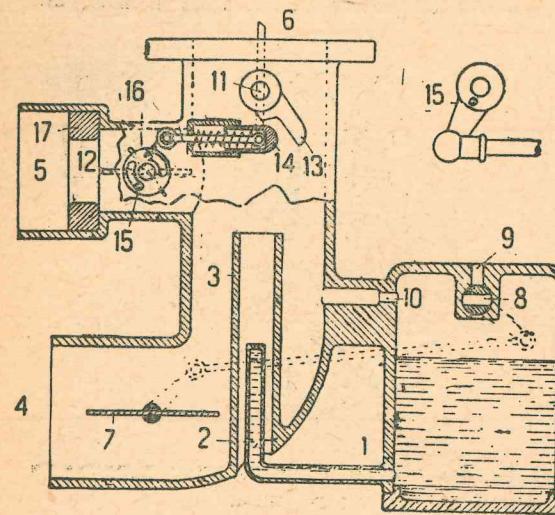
Смеситель Рекс. 1 — поплавковая камера; 2 — жиклер; 3 — трубка диффузора; 4 — вход воздуха; 5 — выход газовоздушной смеси; 7 — дроссель газа; 8 — вентиль поплавковой камеры; 9 — отверстие, соединяющее камеру снаружным воздухом; 10 — отверстие, соединяющее поплавковую камеру с смесителем; 11 — дроссель смеси; 12 — дроссель воздуха; 13 — рычаг связи воздуха и смеси; 14 — связь дросселя смеси с дросселем воздуха; 15 — проводок ручной регулировки; 16 — проводок связи; 17 — постоянная регулировочная шайба
